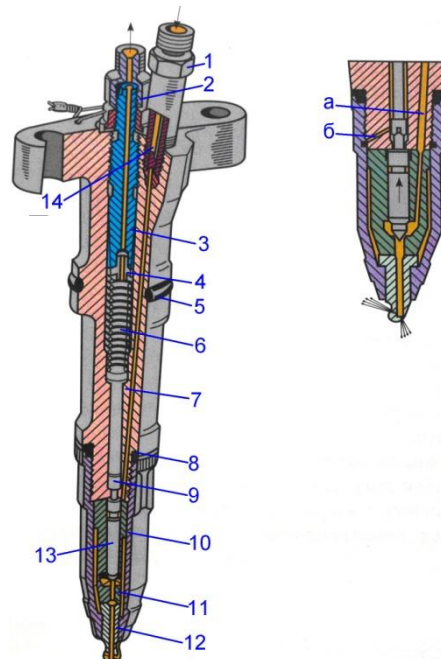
Форсунка дизелей типа 5Д49: 1,2 - штуцера; 3 - регулировочный штуцер; 4 - тарелка; 5, 8 - резиновые кольца; 6 - пружина; 7 - корпус; 9 - толкатель; 10 - колпак; 11 - корпус иглы; 12 - распылитель; 13 - игла; 14 - щелевой фильтр; а, б - каналы размерами проходных сечений в них, числом и размерами сопловых отверстий и габаритными размерами.
